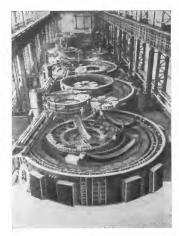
Укрупнительная сборка узлов на сборочной площадке.
